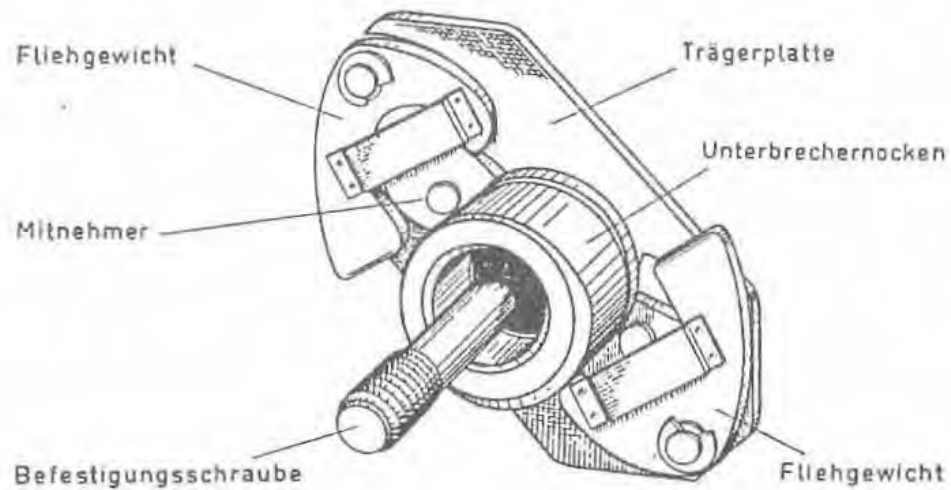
Fliehkraftversteller mit Nocken und Befestigungsschraube (Rückseite)
